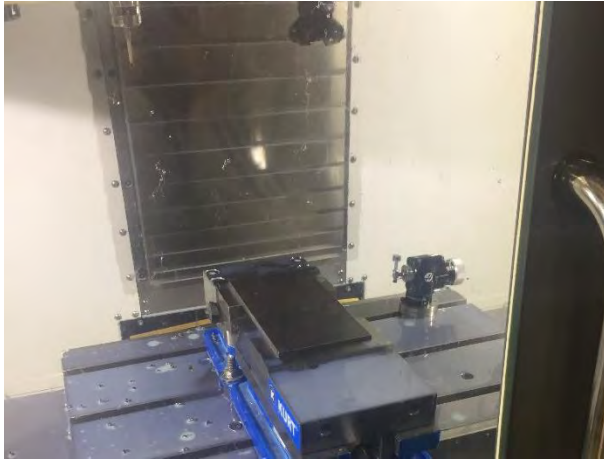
Careado de placas mediante centro de maquinado Haas VF1, corte de cara B.
